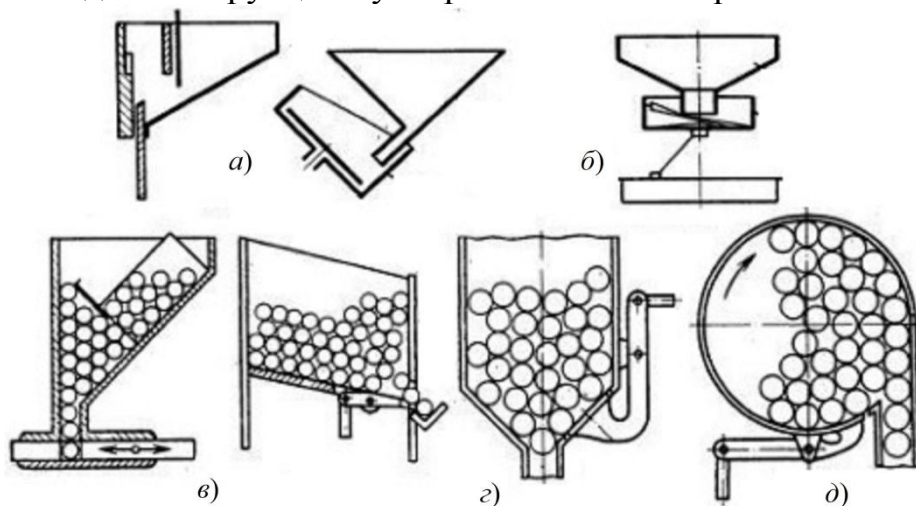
Формы бункеров бункерных загрузочных устройств: *а* – ковшеобразные; *б* – цилиндрические с предбункером; *в* – ящичные ковшеобразные для стержневых заготовок; *г* – ящичные для плоских заготовок; *д* – цилиндрические для плоских заготовок
